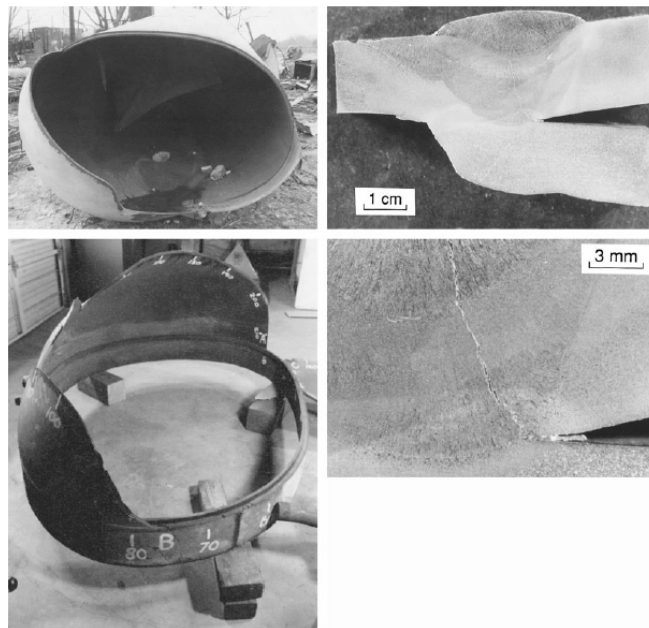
Tubo de propano que explodiu devido a uma trinca na solda. (DOWLING, 2007).
